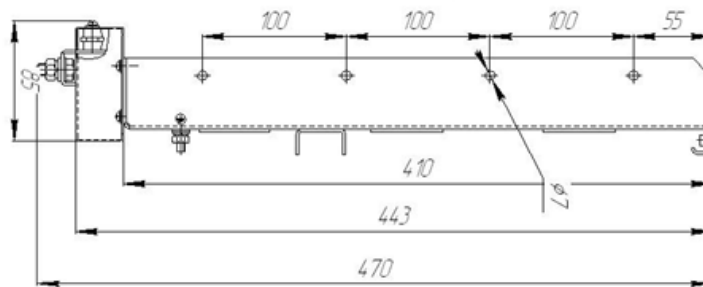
Габаритные и установочные размеры кассеты ЗПУ-10-7
